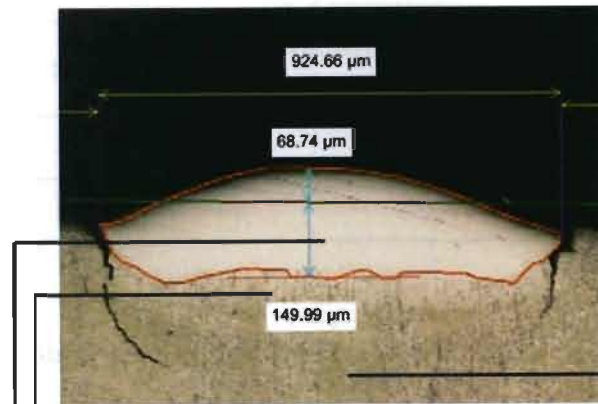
10 Cordón de soldadura 1 visto a 5X
